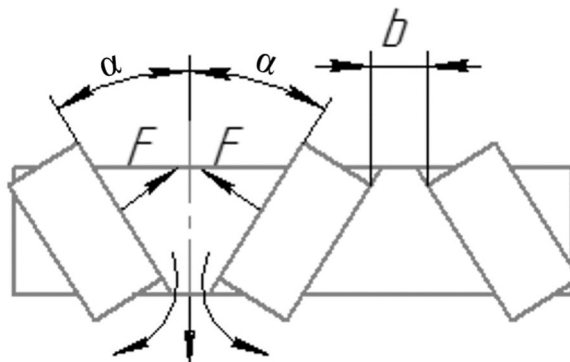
Схема установки лопатки на лопасти и движение смеси
